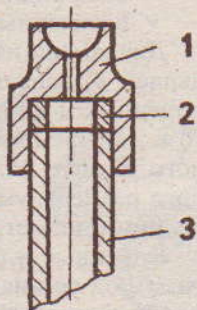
Способ увеличения длины штанги: 1 - наконечник; 2 - вставка; 3 - штанга
